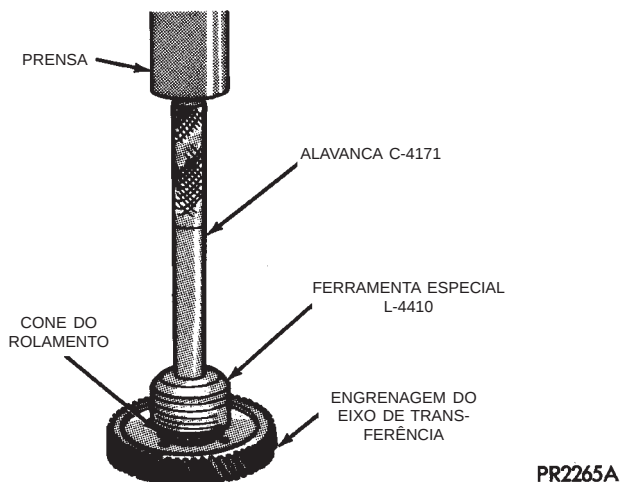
Instalação do Cone de Rolamento da Engrenagem do Eixo de Transferência
